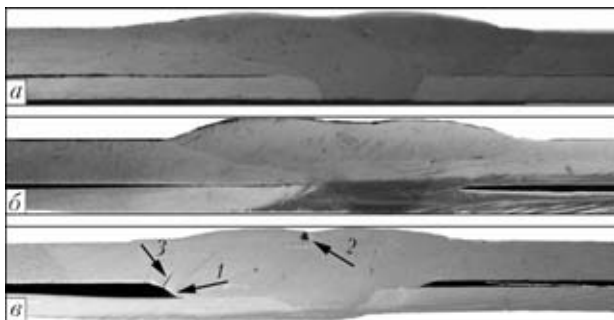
Макрошлифы сварных соединений с зазором 0,1 (а), 0,3 (б) и 0,5 (в) мм: 1 — выплеск в зазор; 2 — усадочная раковина; 3 — трещина
